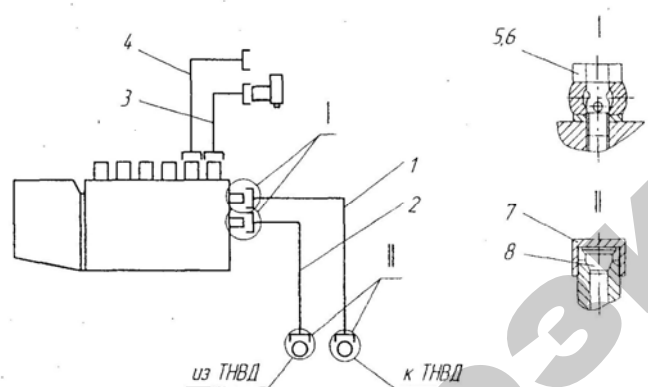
Схема соединений трубопроводов при испытании 4ТМ 8,5×10 (кроме ТНВД двигателя ЯМЗ-740) со стендовым насосом:
